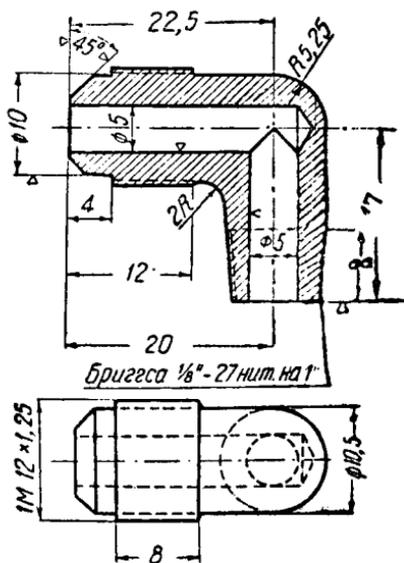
Дет. № 354. Колено трубки в крышку поплавковой камеры для воды
